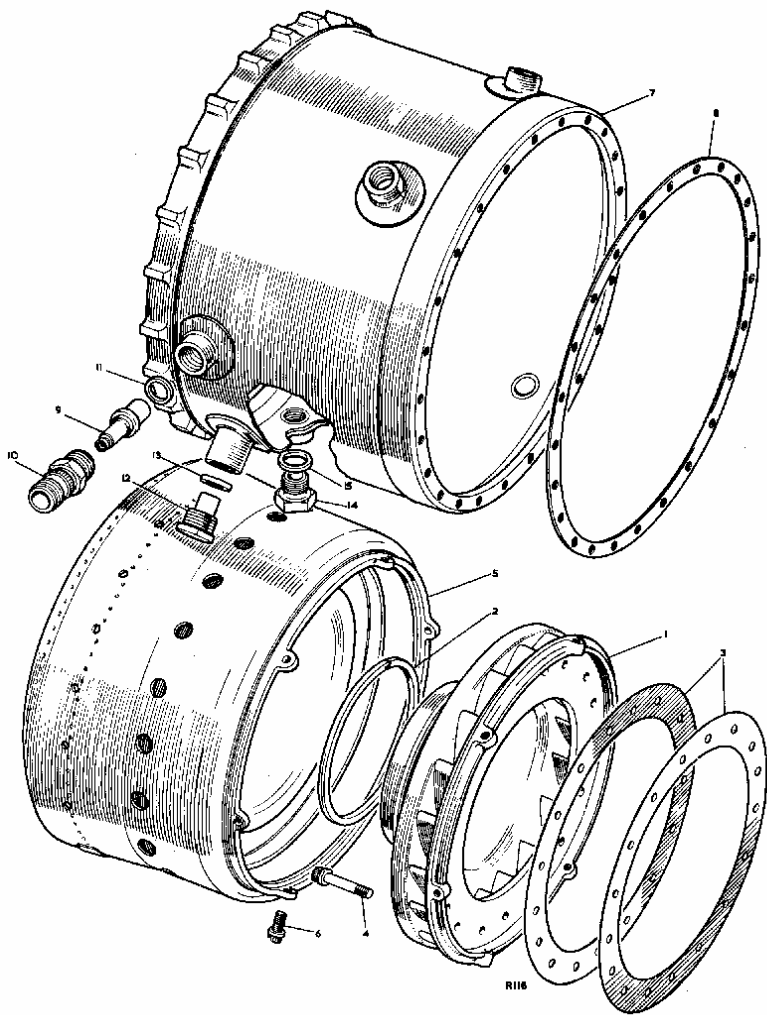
Explosionszeichnung der Brennkammer [5]
